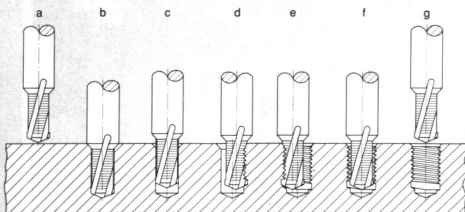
Arbeitsablauf beim Bohrgewindefräsen
